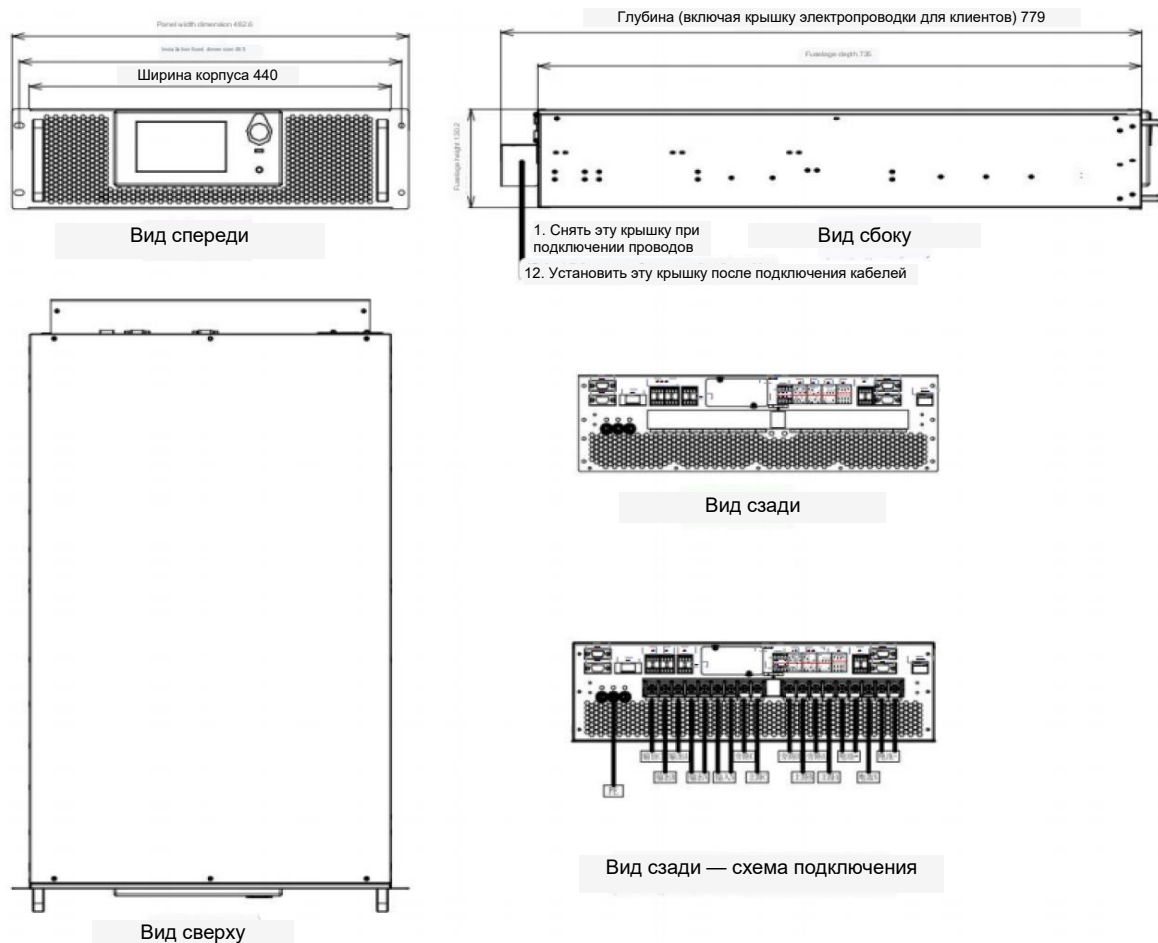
Габаритный чертеж 10-30 кВА
